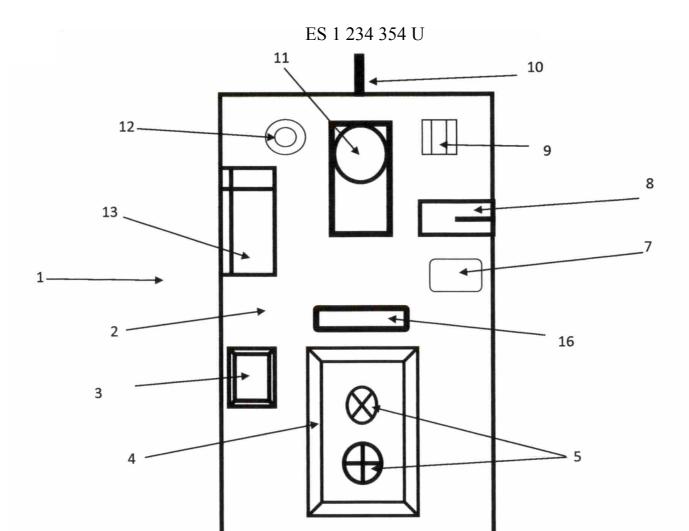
Muestra una vista en alzado del dispositivo cargador de vehículos eléctricos instalado en un elemento de iluminación.
